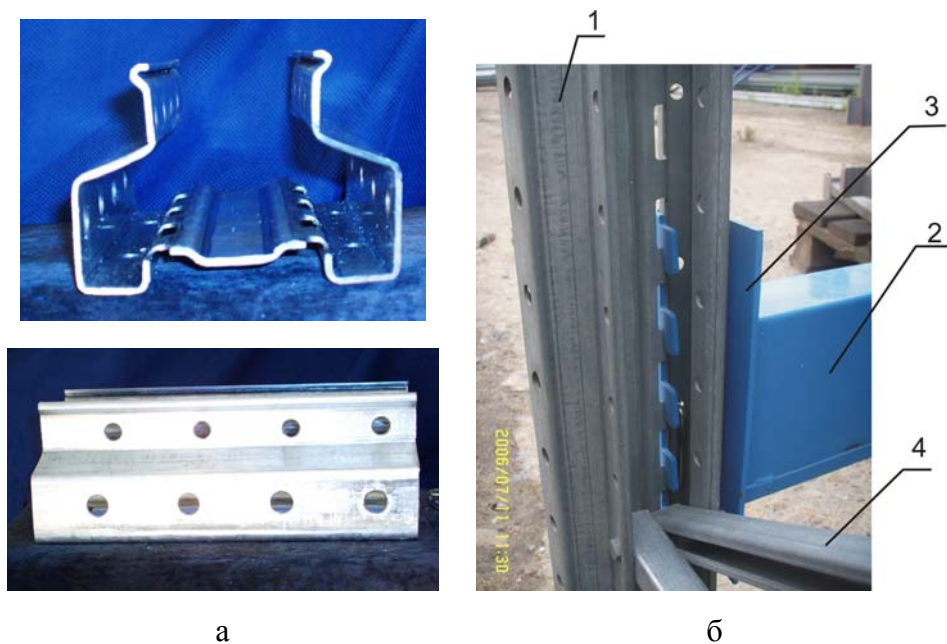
Готовый профиль (вид с торца и сбоку) (а) и сборочный узел (б) на основе профиля «Стойка»: 1 – стойка 110x77x2 мм, 2 – балка, 3 – зацеп, 4 – распорка
